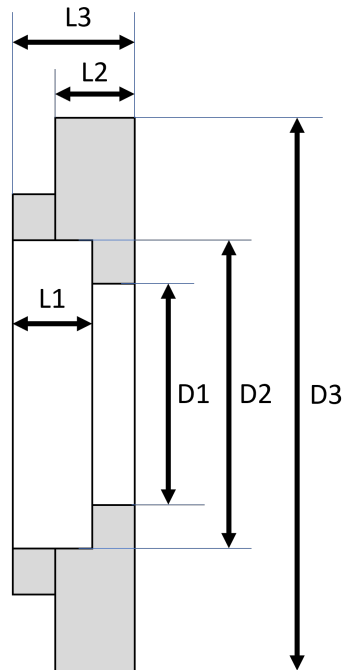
Dimensions des carters latéraux pour les calculs des résistances
